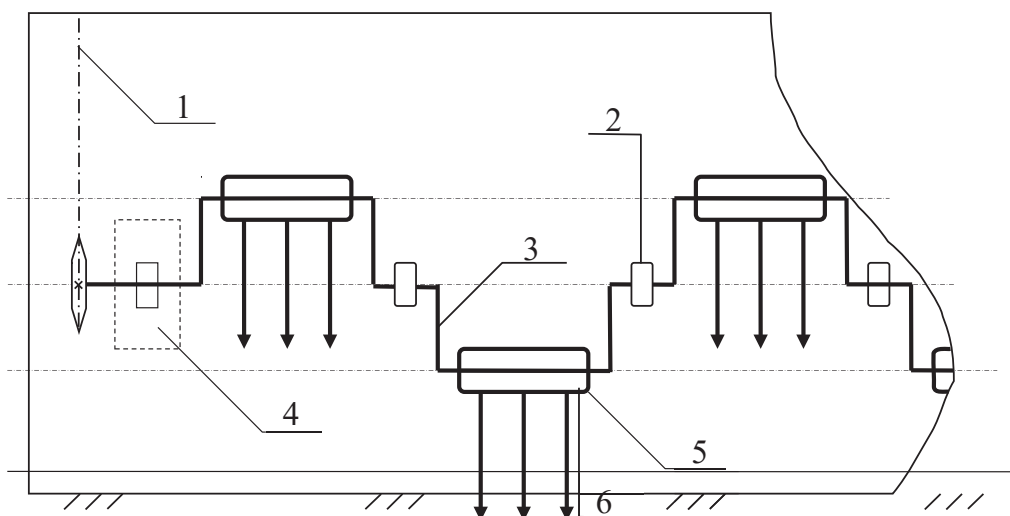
Схема конструкции адаптера для борьбы с гололедицей: 1 – цепная передача; 2 – соединительная муфта; 3 – промежуточный коленчатый вал; 4 – кронштейн; 5 – ударное устройство; 6 – тыльная сторона отвальной поверхности.
